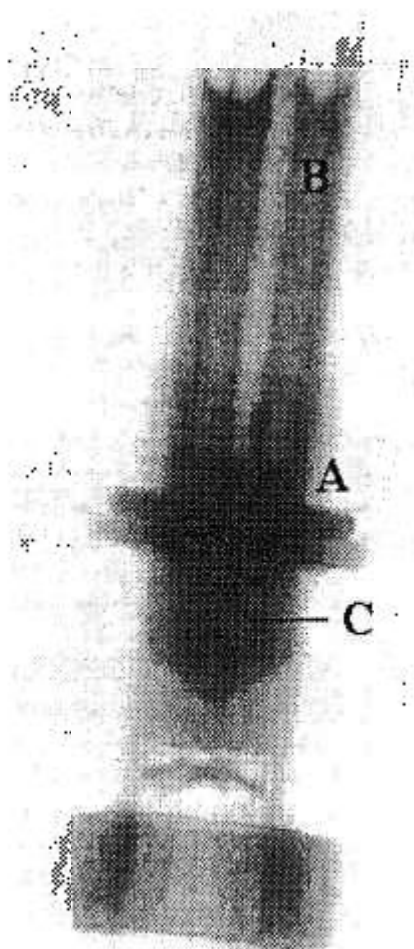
Componente pirotécnico "parafuso explosivo" do CTA: A) invólucro de aço; B) material explosivo; C) adesivo.
